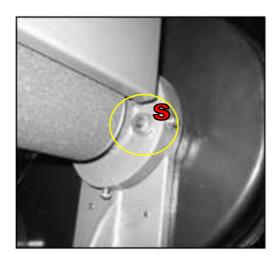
Dado di bloccaggio telaio porta-nastro Art. 0662.
